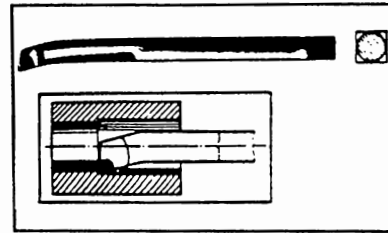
Herramienta con cabeza de corte de una sola pieza.
